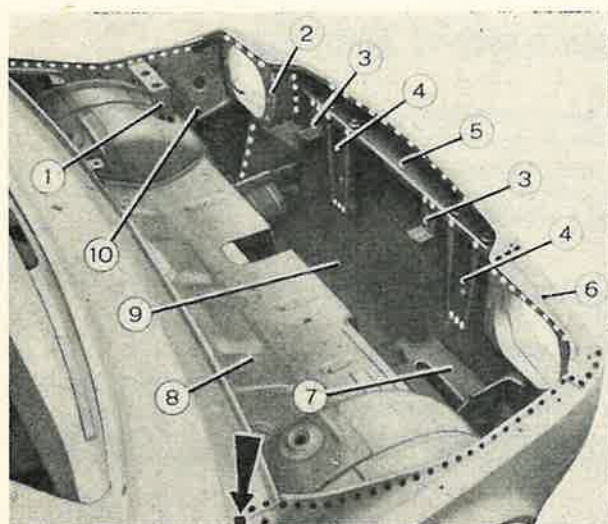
Liaisons par points de soudure des pièces composant le coffre à bagages.
